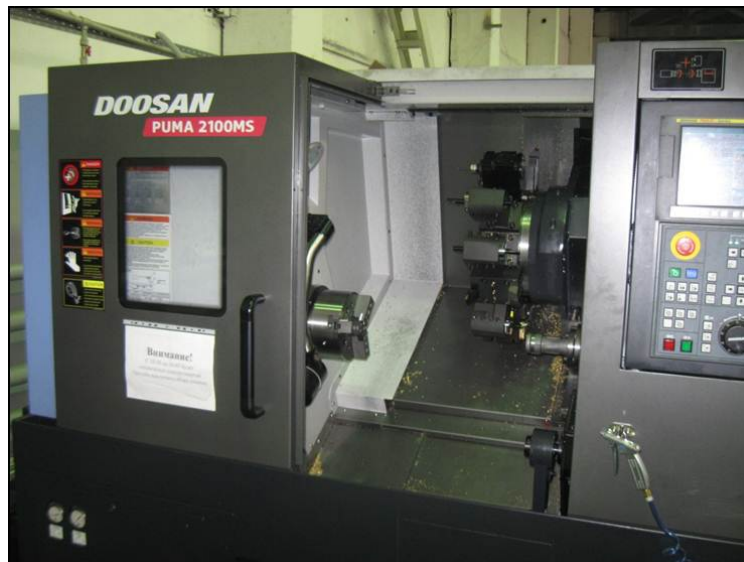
Високопродуктивний двошпindelний токарний обробний центр PUMA 2100MS з приводним фрезерним інструментом і контр-шпинделем ("DOOSAN")
